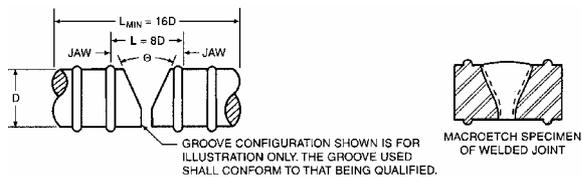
Sección a realizar ensayo de tracción y microscopia para calificación de soldador y proceso de soldadura.
